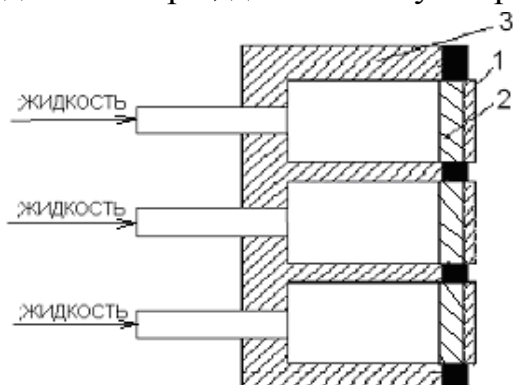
Схема гидравлической присадки ножей гарнитуры: 1 – нож; 2 – плунжер; 3 – диск с камерами
